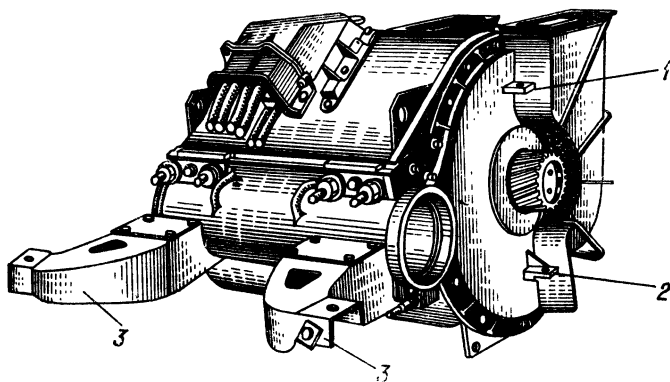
Двигатель однофазного тока с двусторонней зубчатой передачей
